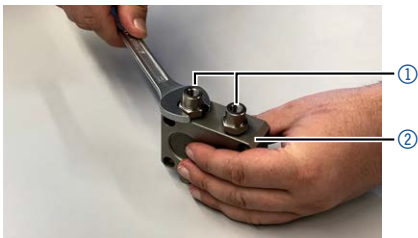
Entfernen der oberen Buchsen (Ausgangverschraubungen)
